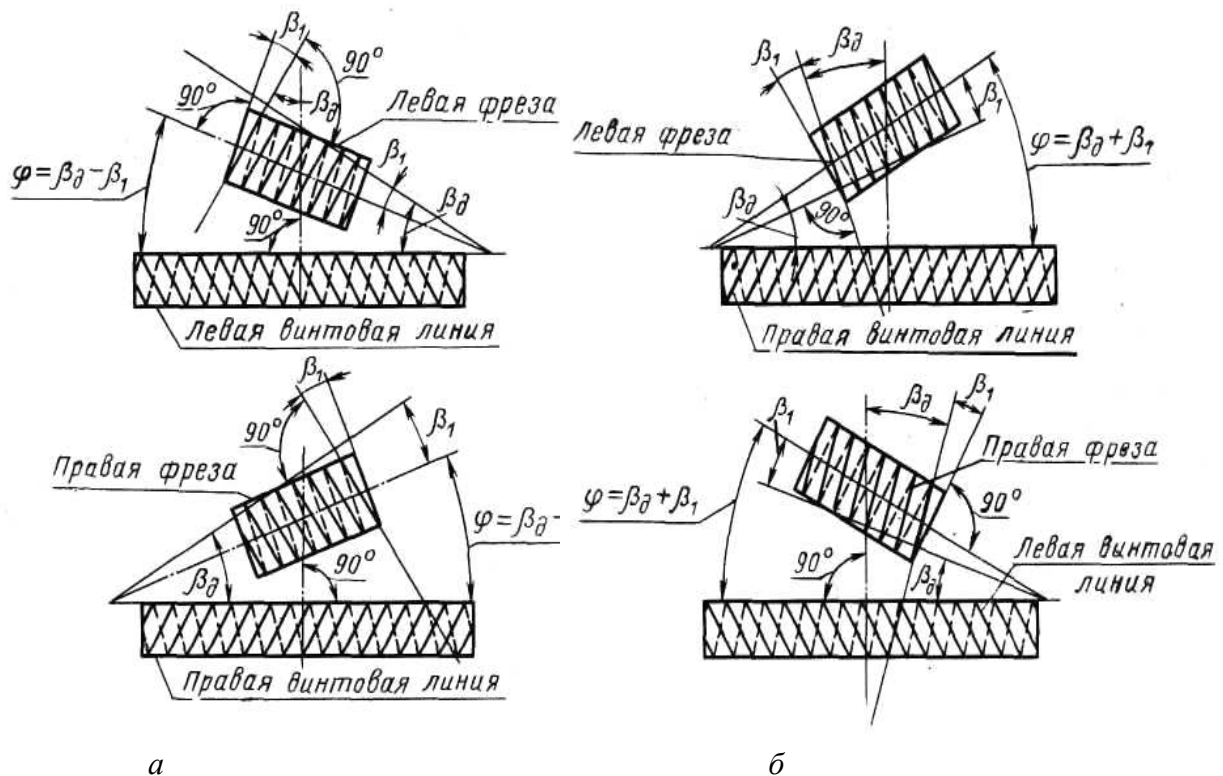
Взаимное расположение червячной фрезы и заготовки при нарезании цилиндрического колеса с винтовой нарезкой
